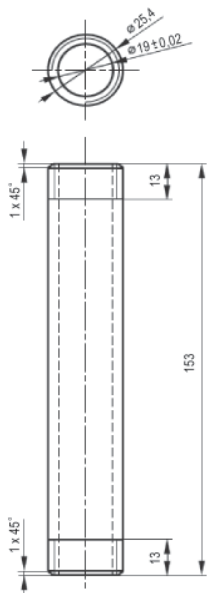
Деталь 4 – Стабилизирующая трубка
